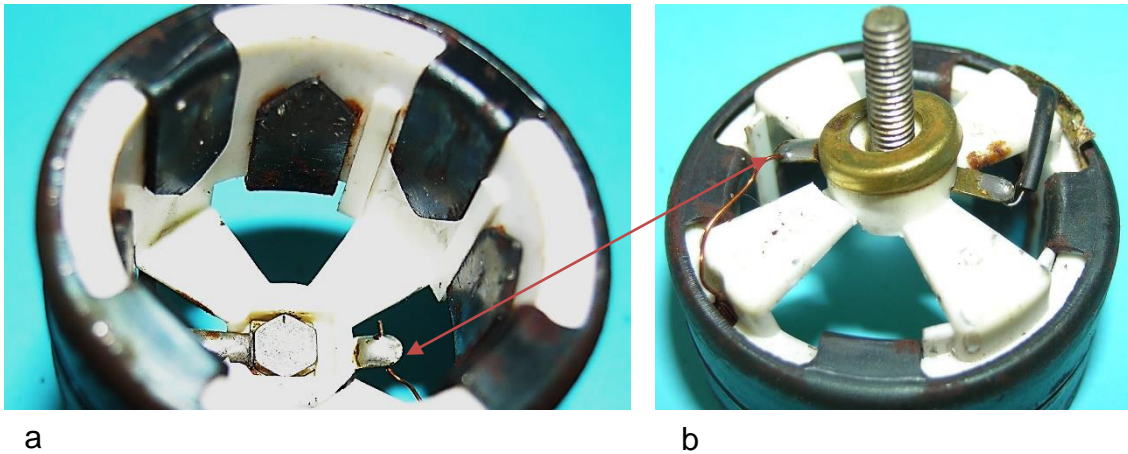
Kontakte am Kabelanschlussbolzen: a) Schraubenkopf des Kabelanschlussbolzens, b) Massekontaktring
